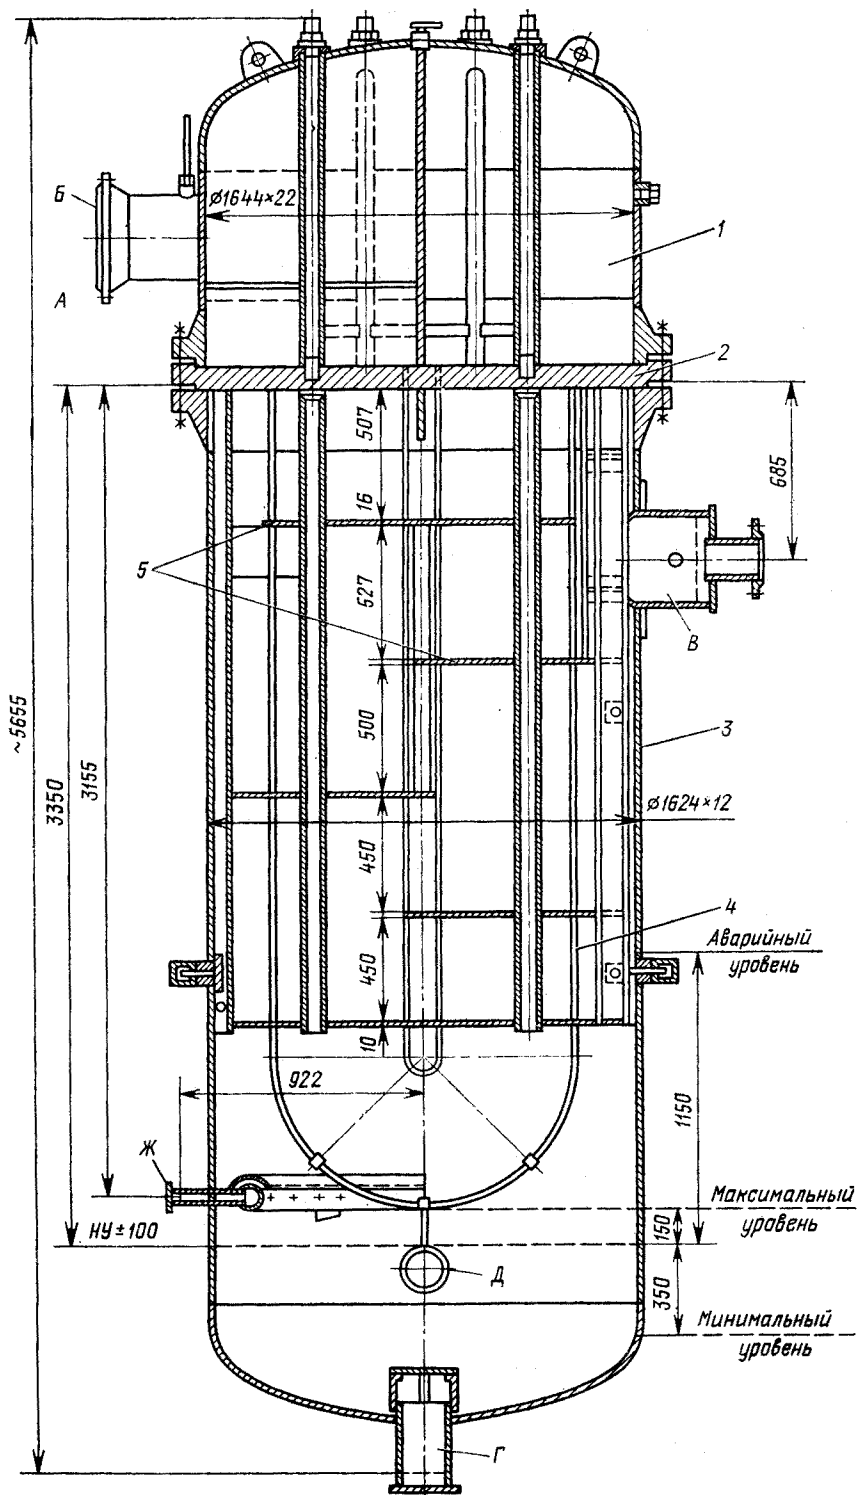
Подогреватель ПН-400-26-8-V:
